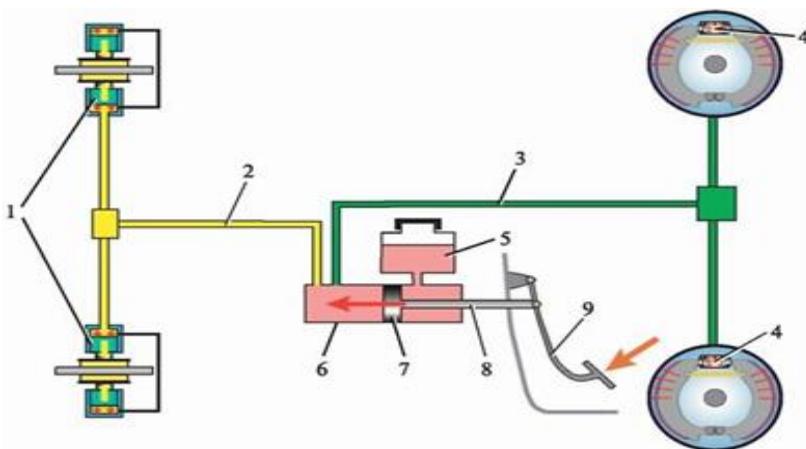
Схема гидропривода тормозов: 1 – тормозные цилиндры передних колес; 2 – трубопровод передних тормозов; 3 – трубопровод задних тормозов; 4 – тормозные цилиндры задних колес; 5 – бачок главного тормозного цилиндра; 6 – главный тормозной цилиндр; 7 – поршень главного тормозного цилиндра; 8 – шток; 9 – педаль тормоза
